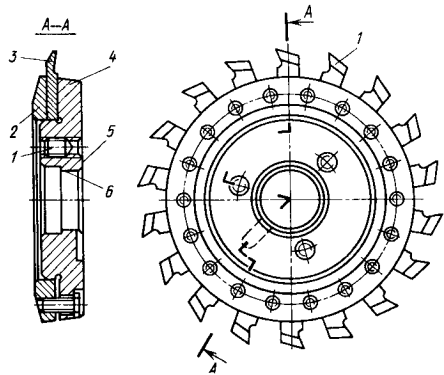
Резцовая головка для нарезания прямозубых конических колес
